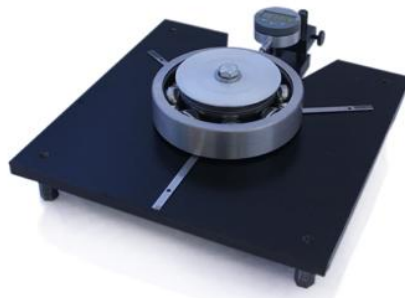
Пристосування для вимірювання радіального зазору підшипника
